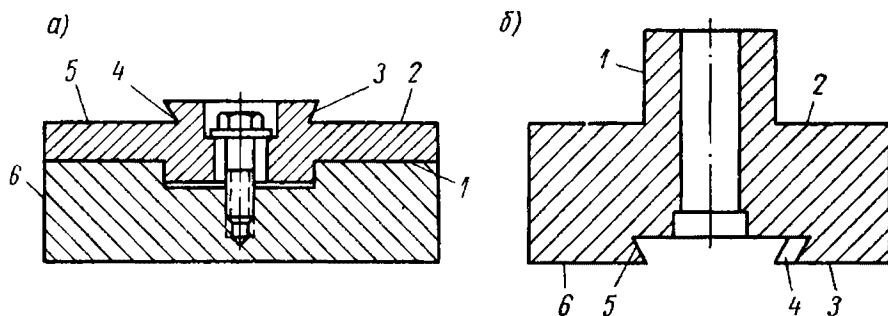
Салазки суппорта: а — поворотные, скрепленные с приспособлением; б — верхние
